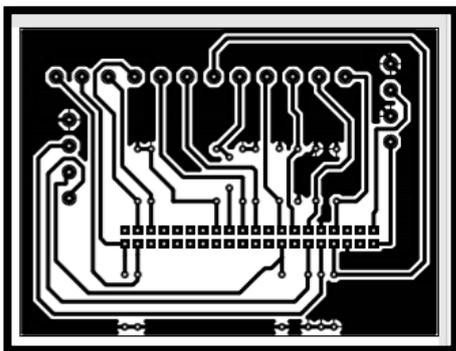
PCB 2, diseñado para encajar directamente en la tarjeta controladora Raspberry.
